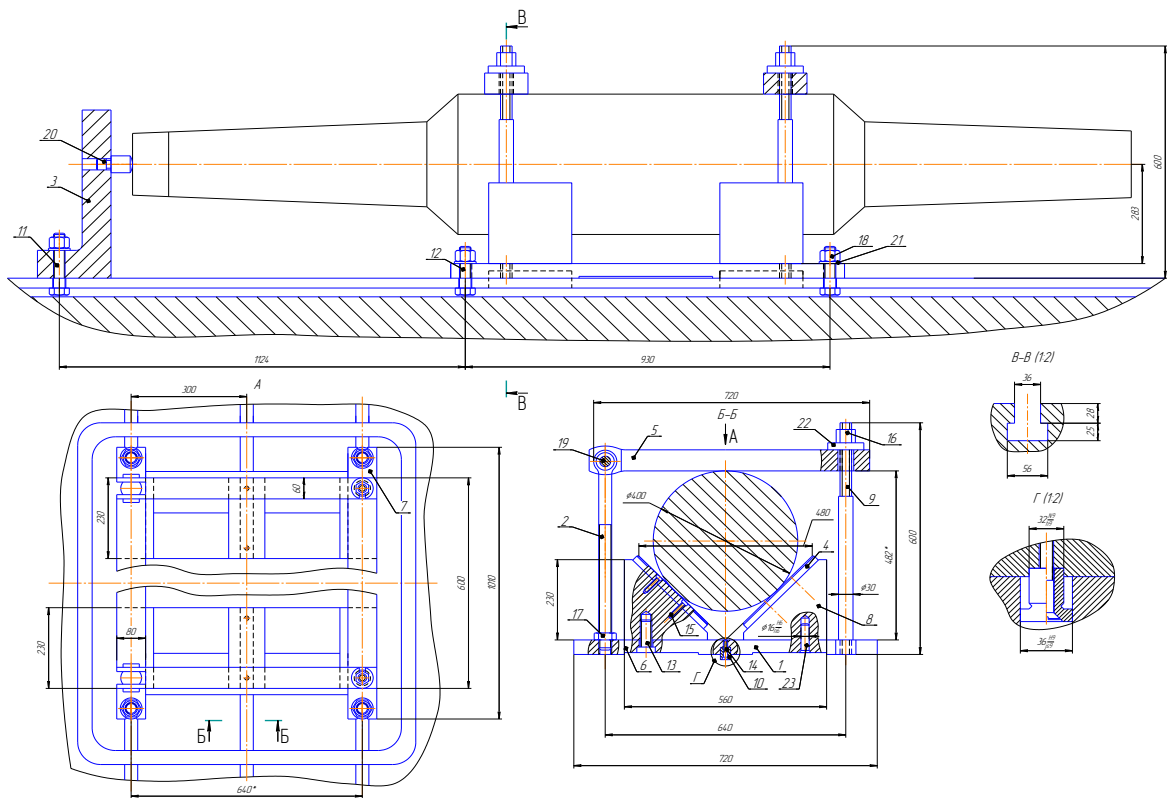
Ескіз пристосування для закріплення групи деталей: 1 – основа; 2 – болт відкидний; 3 – кутник; 4 – накладка на призму; 5 – планка відкидна; 6 – планка повздовжня; 7 – планка поперечна; 8 – призма опорна; 9 – шпилька; 10 – шпонка; 11 – болт; 12 – болт; 13 – болт; 14 – гвинт; 15 – гвинт; 16 – гайка; 17 – гайка; 18 – гайка; 19 – заклепка; 20 – опора постійна зі сферичною головкою; 21 – шайба плоска; 22 – шайба швидкозмінна; 23 – штифт.
